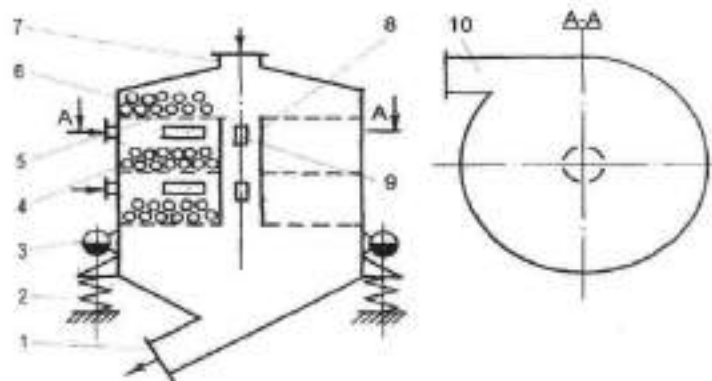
Схема тарілкового вібромлина: 1,7- патрубки для завантаження та розвантаження; 2 - пружна опора; 3 -вібробуджувач; 4 - мелюче тіло; 5 - перфорована тарілка; 6 - робочий контейнер; 8 -гільза; 9 - ярусні щілини; 10 - патрубки пневмовводу
